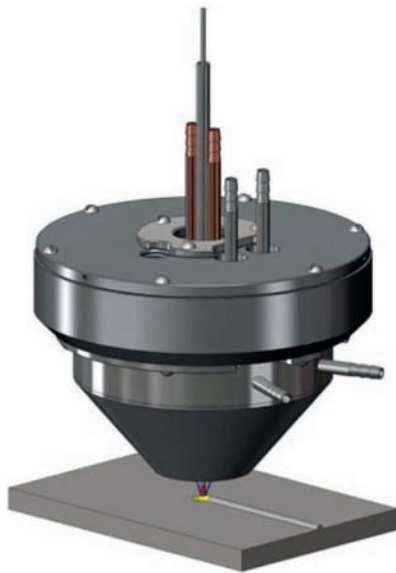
Схема объединённого узла нагрева и подачи присадочного материала, используемого в xBeam 3D Metal Printer и сходилась максимально близко к поверхности формируемой конструкции. Это позволяет реализовать эффективное и достаточно равномерное расплавление присадочной проволоки без существенного перегрева, а также обеспечить сопутствующий подогрев области наплавки для активации поверхности твердого металла перед его контактом с жидким присадочным материалом. Процесс проходит в условиях глубокого вакуума, что позволяет эффективно фокусировать электронный луч и избежать загрязнения металла примесями в случае его высокого сродства с кислородом и/или азотом. Подложка формируемого изделия помещается в силовую оснастку, которая прижимает ее к подвижной платформе, перемещает относительно неподвижного источника нагрева с заданной скоростью в плоскости подложки и периодически по мере наплавки каждого валика в перпендикулярном направлении.
